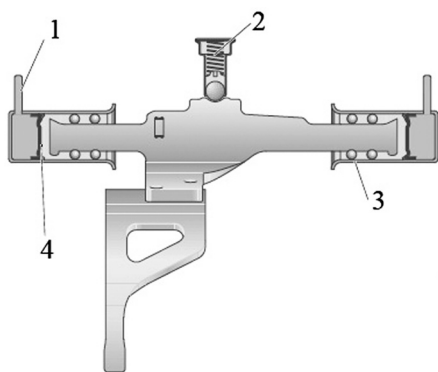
Исполнительный механизм автоматизированной КП DSG Volkswagen: 1 — подача масла; 2 — фиксатор; 3 — гидроцилиндр; 4 — поршень
